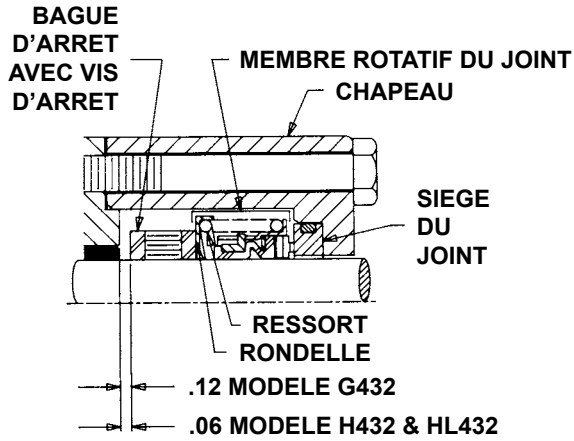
VUE EN COUPE, SECTEUR DU JOINT
